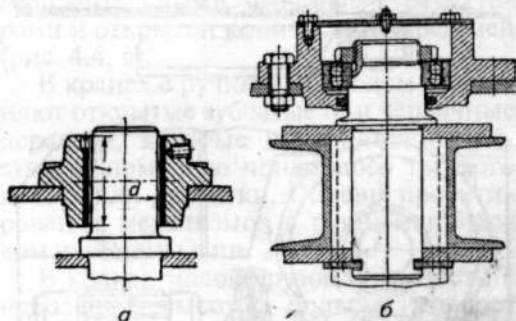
Конструкции верхней опоры поворотной колонны:
